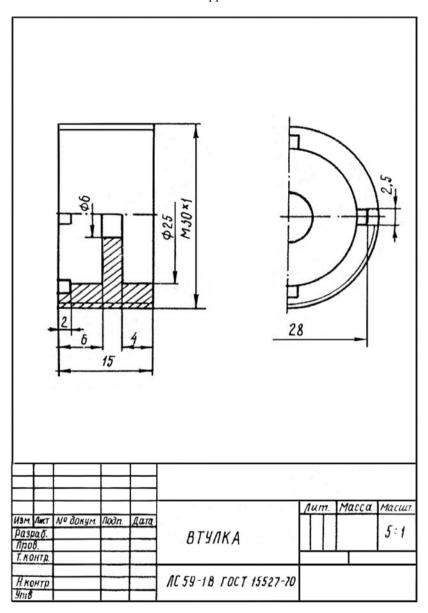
Рабочий чертеж втулки (деталь поз. 3)
